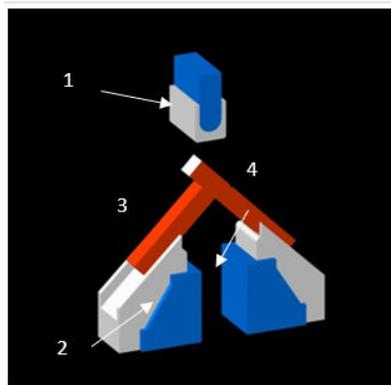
Desain 2 dimensi *Jig and Fixture* untuk uji *bending* tampak depan
